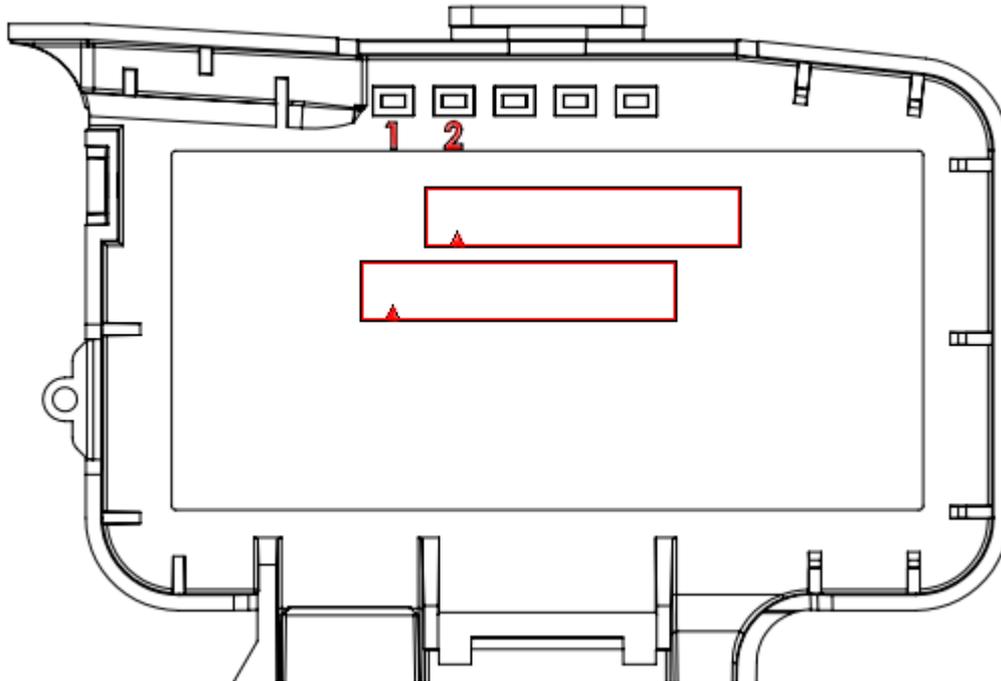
Montaje lateral del adaptador (superposiciones) al grabador MacR6 (se necesitan 1 TORX T10 3x16 adicional, 1 tornillo TORX T10 3x6)
